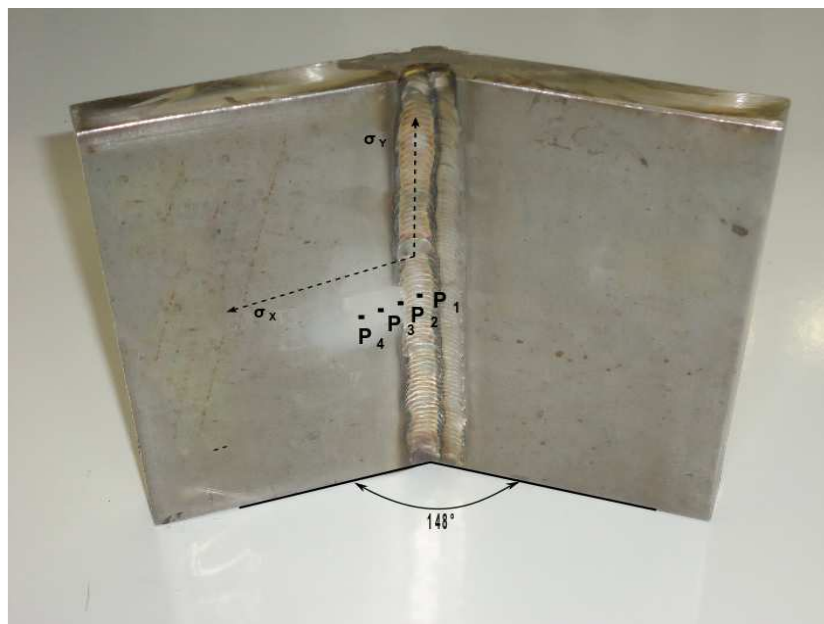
Corpo de prova 1 – Chapas de Aço Inoxidável Duplex 2205 após o processo de soldagem GTAW.
